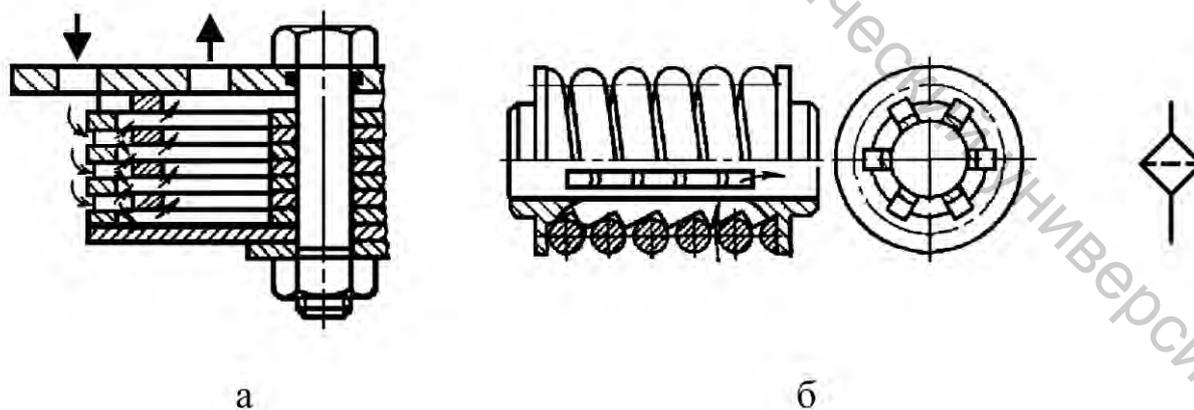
Фильтры: пластинчатый (а) и проволочный (б)
